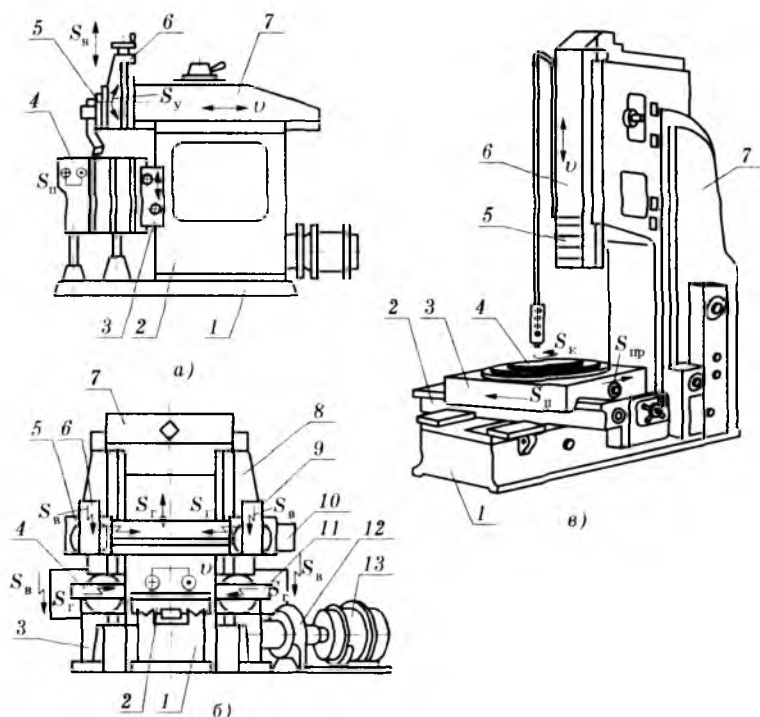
Схемы конструкций строгальных и долбежных станков:
